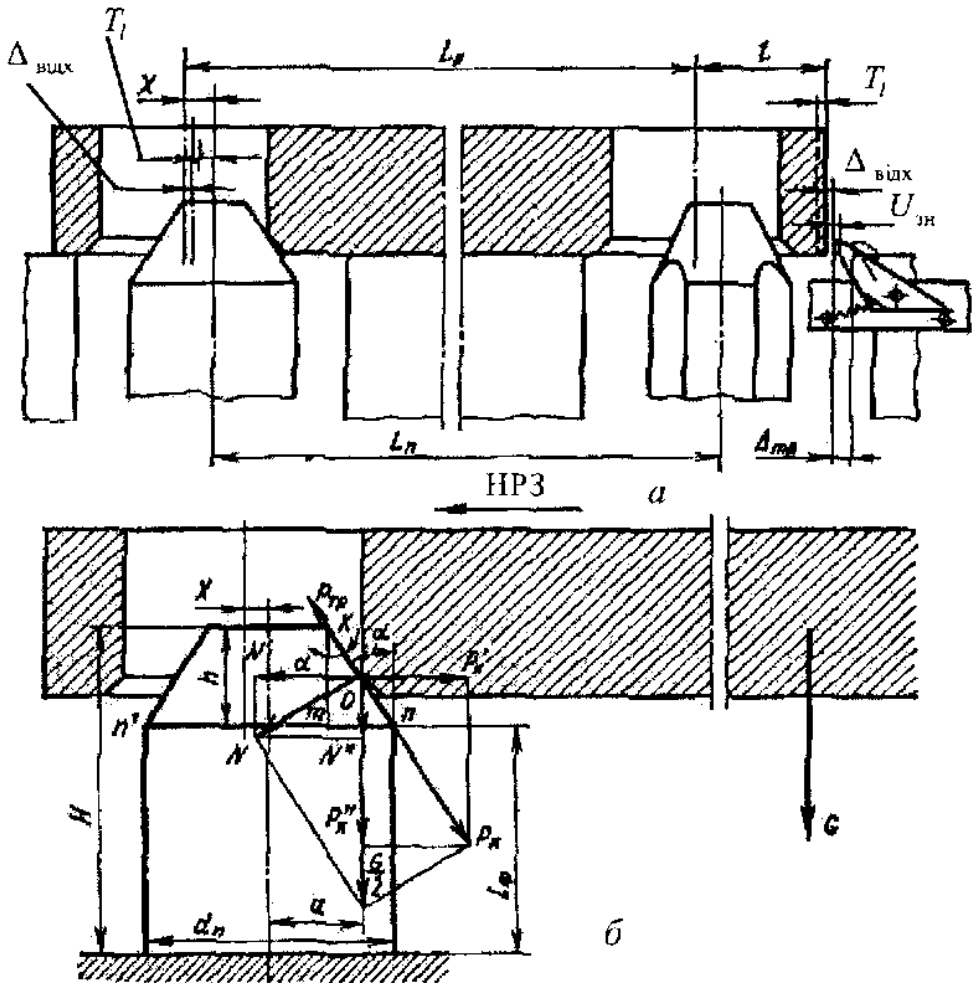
Фіксація заготовки в робочій позиції:
